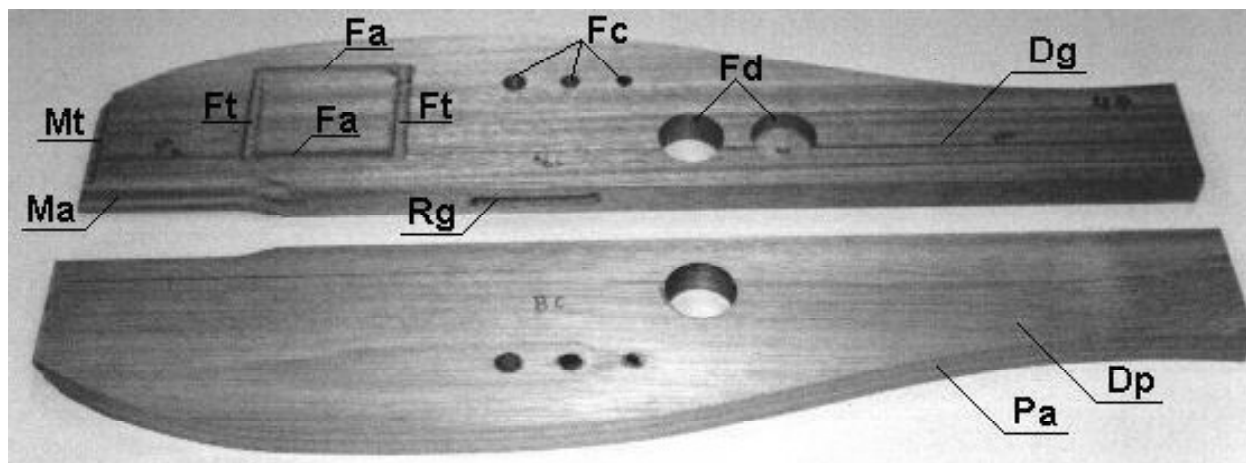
Corpo-de-prova dos ensaios de usinagem, em que Dp= desempenho; Dg= desengrosso; Ma= moldura axial “parada”; Mt= moldura no topo; Pa= perfilagem axial sinuosa (com faca plana); Rg= rasgo (furadeira horizontal); Fa= fresamento axial; Ft= fresamento transversal; Fc= furação para cavilha; Fd= furação para dobradiça.
